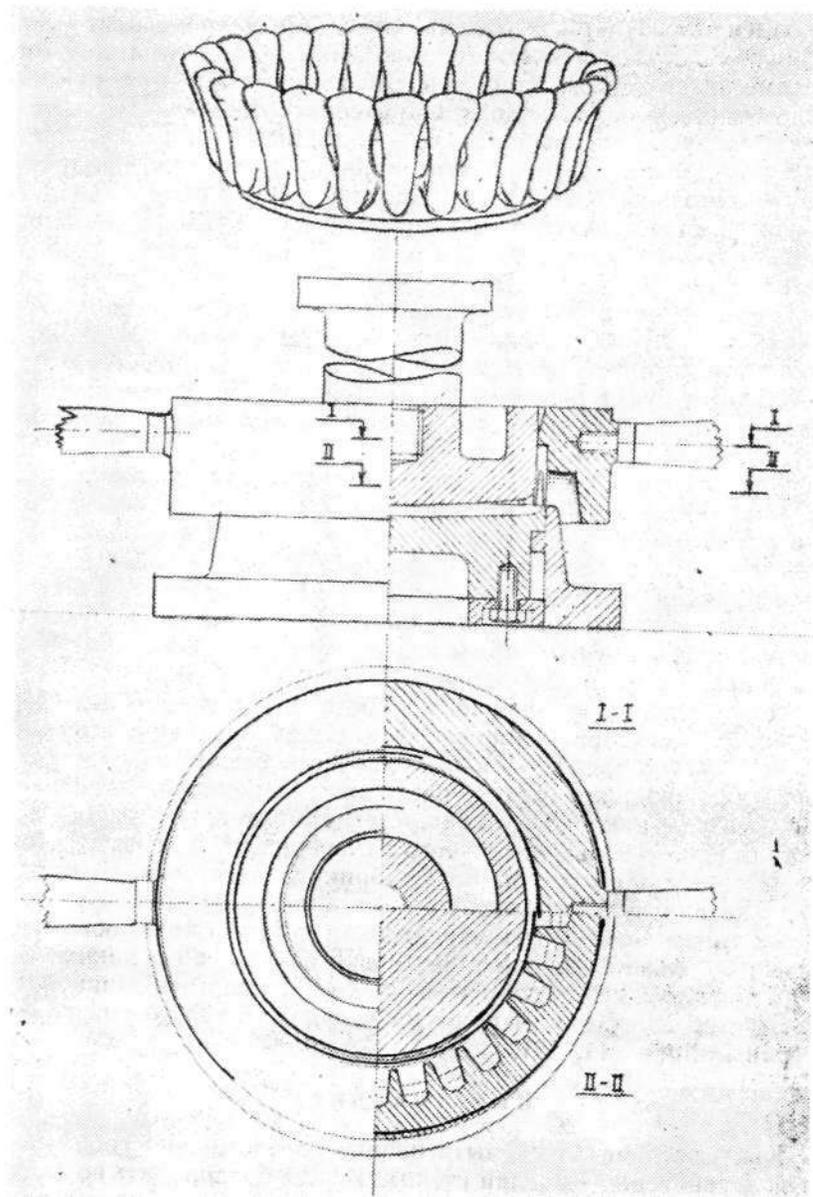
Образец «свободного» прессования и пресс-форма для него.
